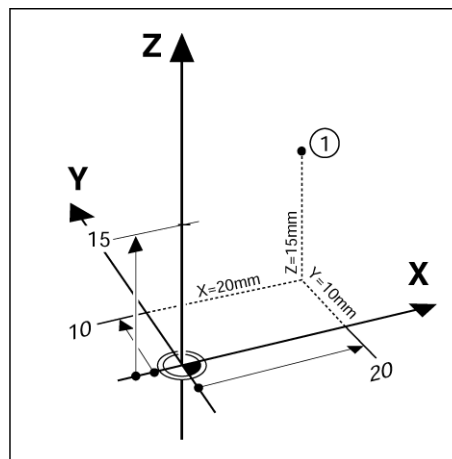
Posición 1 por ejemplo "Posiciones absolutas de la pieza"
